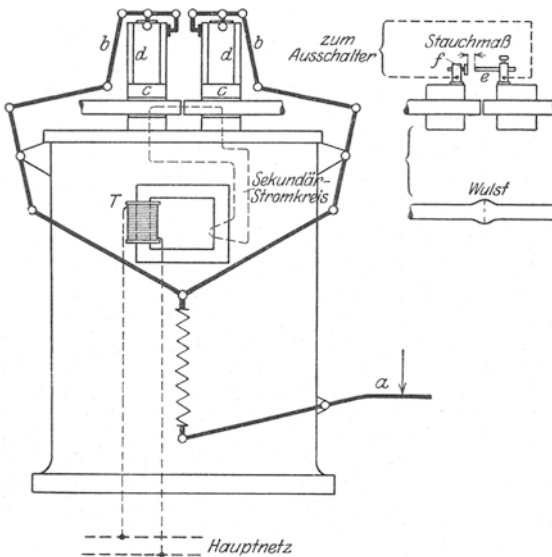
Schema einer Stumpfschweißmaschine.
